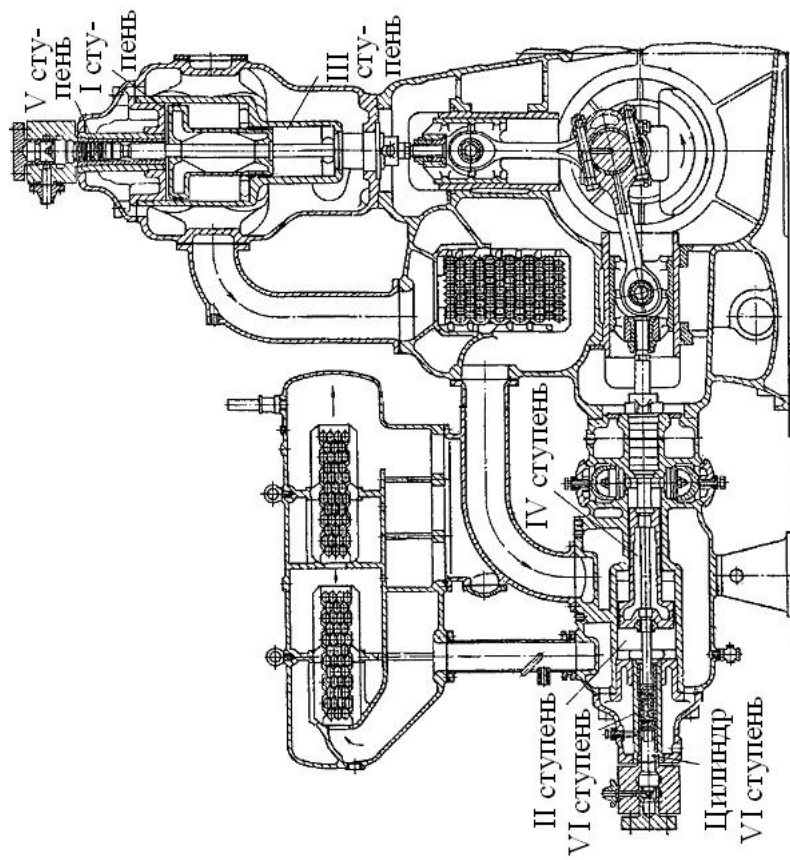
Угловой шестиступенчатый поршневой компрессор
